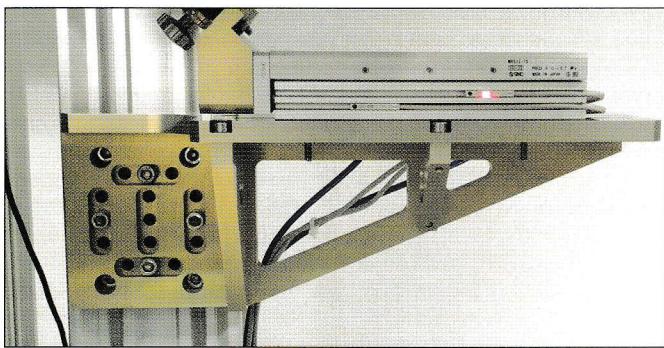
Držák pneumatického stolku testovaný v laboratoři
